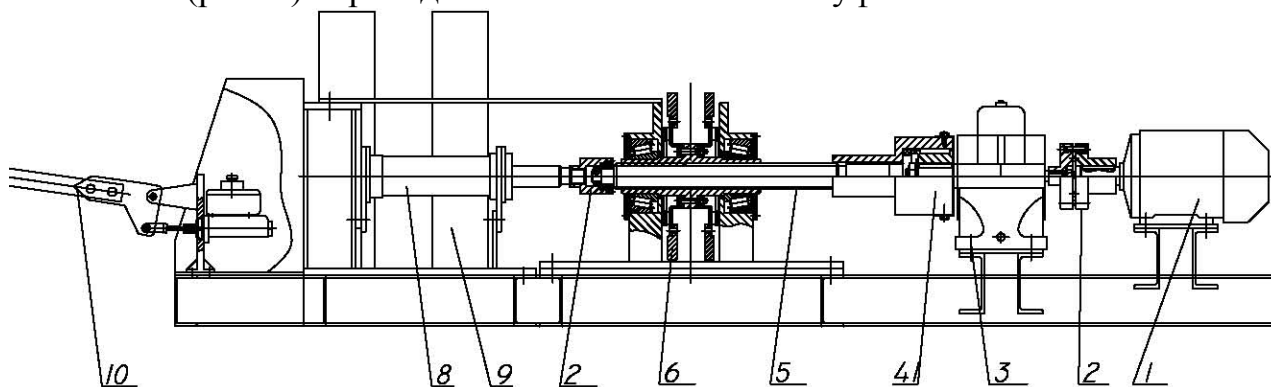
Схема экспериментального стенда: 1 – электродвигатель; 2 – муфта соединительная; 3 – редуктор; 4 – шлицевая втулка; 5 – винт; 6 – гайка с дисковыми тормозами; 7 – упорный подшипник; 8 – гидроцилиндр; 9 – гидросистема муфты; 10 – нагрузочные рычаги
